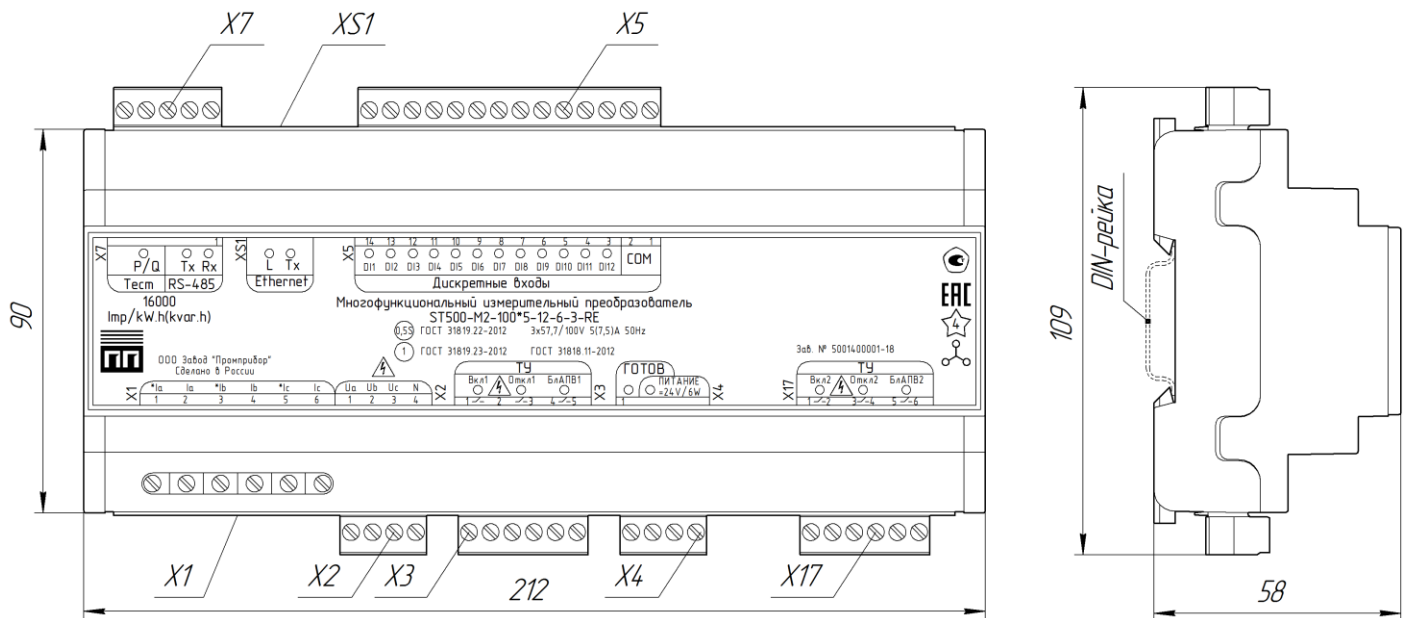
Внешний вид и габаритные размеры МИП ST500-M2-XXX*X-12-6-3-RE и ST500-M2.02-XXX*X-12-6-3-RE
